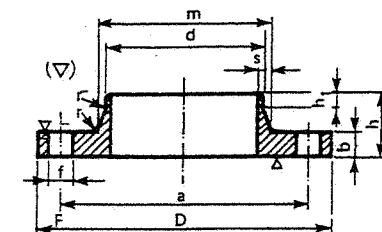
Flangia a collare per tubazioni da saldare di testa.
